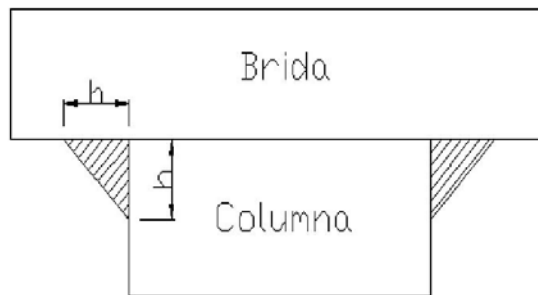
44. Parámetro h de la soldadura. Fuente: Los Autores.
